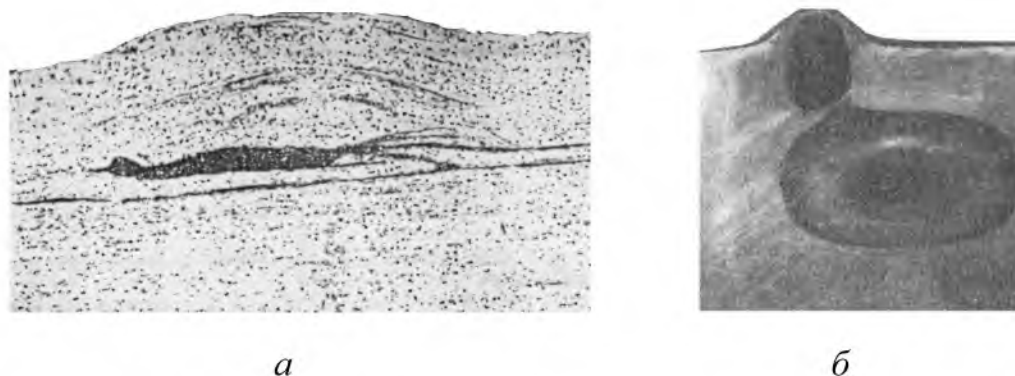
Пузыри от наслоений (а) и запрессовки воздуха (б)
